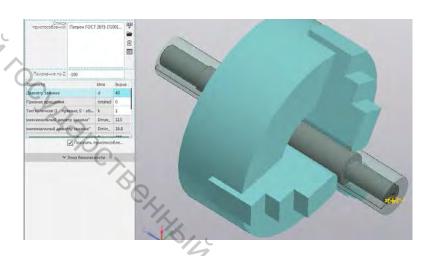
Создание приспособления для закрепления заготовки и задание его положения в первом установе
